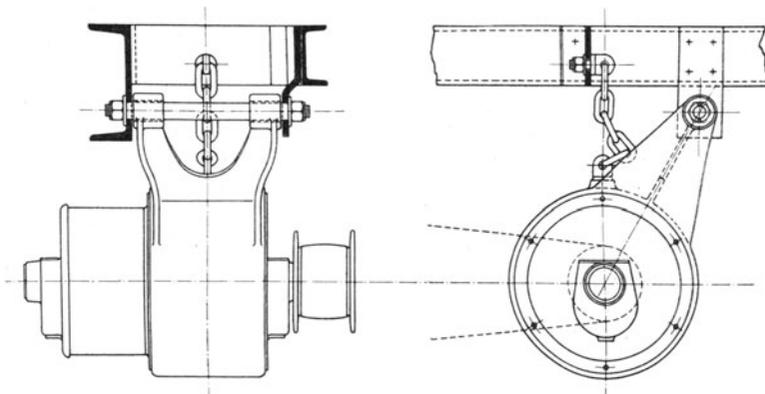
Maschinenaufhängung der Schweizer Bundesbahn für zwei- und dreiachsige Wagen.
